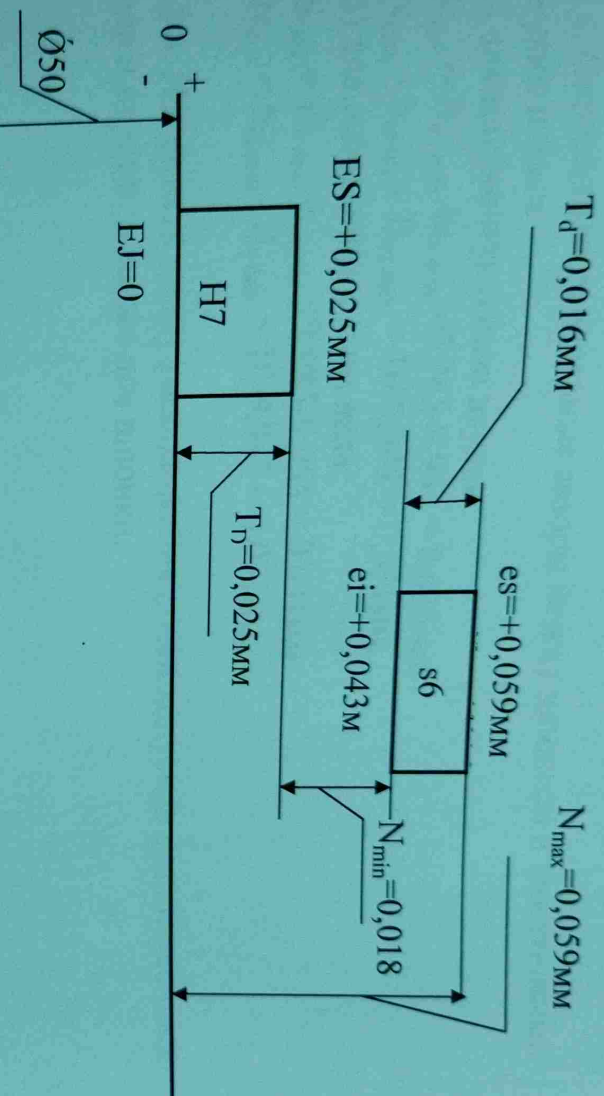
Схема расположения полей допусков для отверстия и вала.
